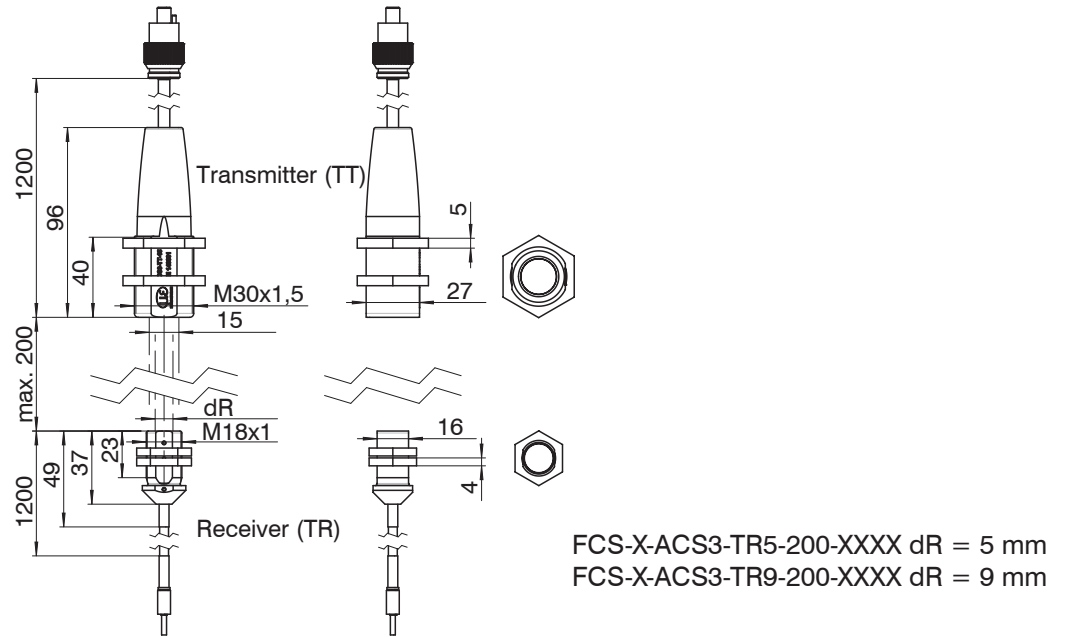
Maßzeichnung FCS-X-ACS3-TRX-200-XXXX (Empfänger), FCS-X-ACS3-TT15-200-XXXX (Sender)
